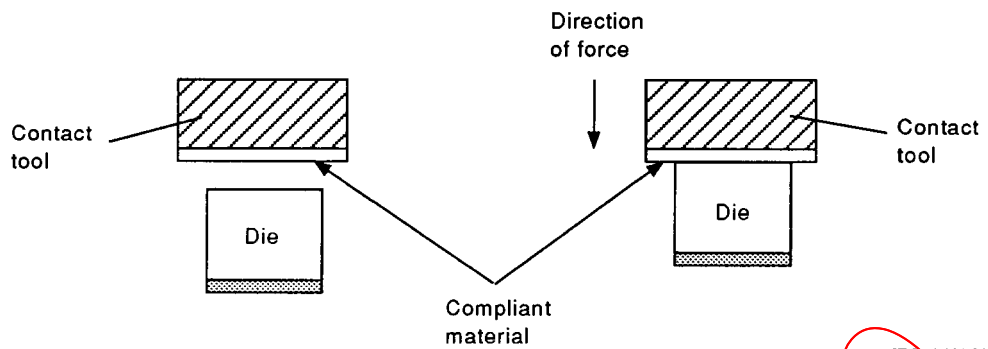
Alignement de l'outil avec la pastille (vue de dessous)
